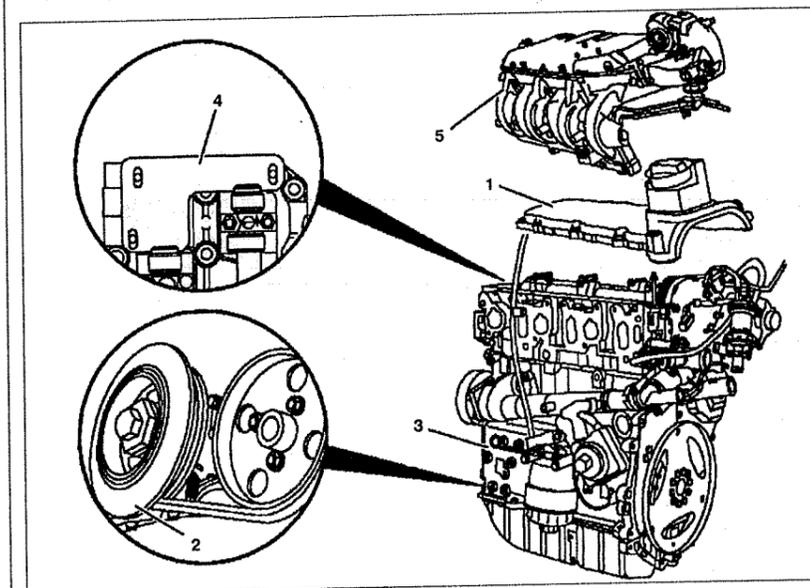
Проверка основного положения распределительных валов: 1. Крышка головки блока цилиндров, 2. Канавочный шкив коленчатого вала, 3. Блок цилиндров, 4. Установочный инструмент, 5. Впускной коллектор.
